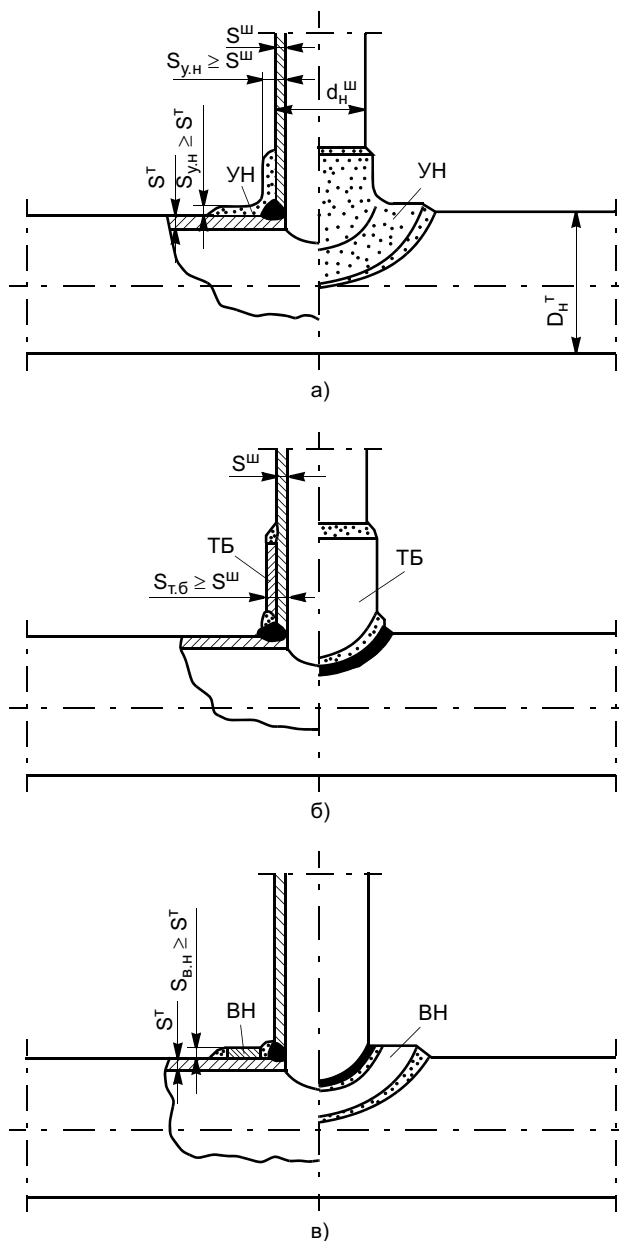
Укрепление тройникового сварного соединения (и врезки труба в трубу): а — нанесение усиливающей наплавки воротникового типа; б — приварка к штуцеру трубчатого бандажа; в — приварка к трубе воротниковой накладки (ВН)
